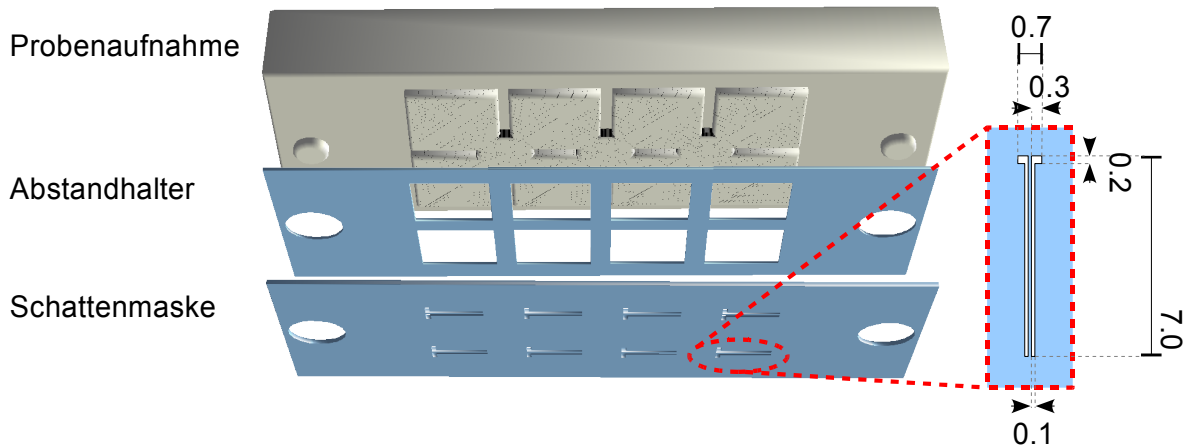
Probenbefestigung in der Aufdampfkammer für acht Proben mit einer Schattenmaske zur Strukturierung von Linienelektroden. Längenangaben in mm.
